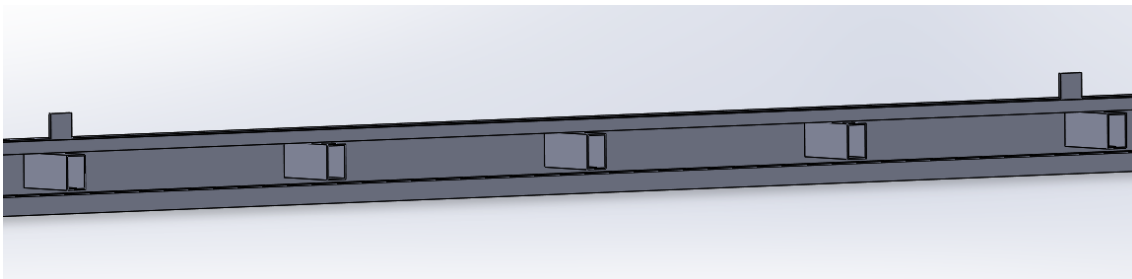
Detalle de las pestañas en las vigas longitudinales del suelo
